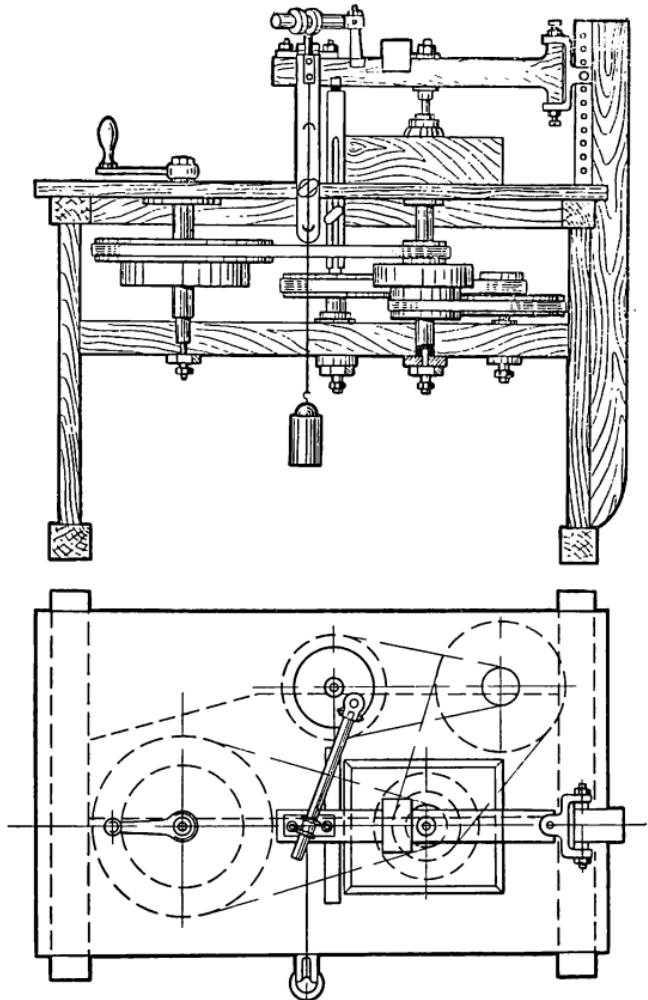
Станок для полировки линз конструкции Й. Фраунгофера
